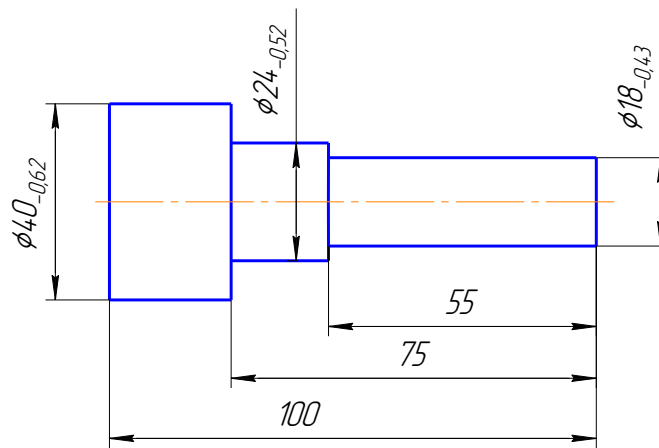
Розташування деталі на кресленку, що обмежена поверхнями обертання
